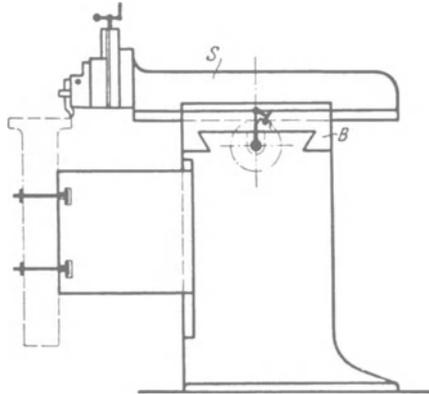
Stößelhobelmaschine mit Querschaltung des Stößels.
